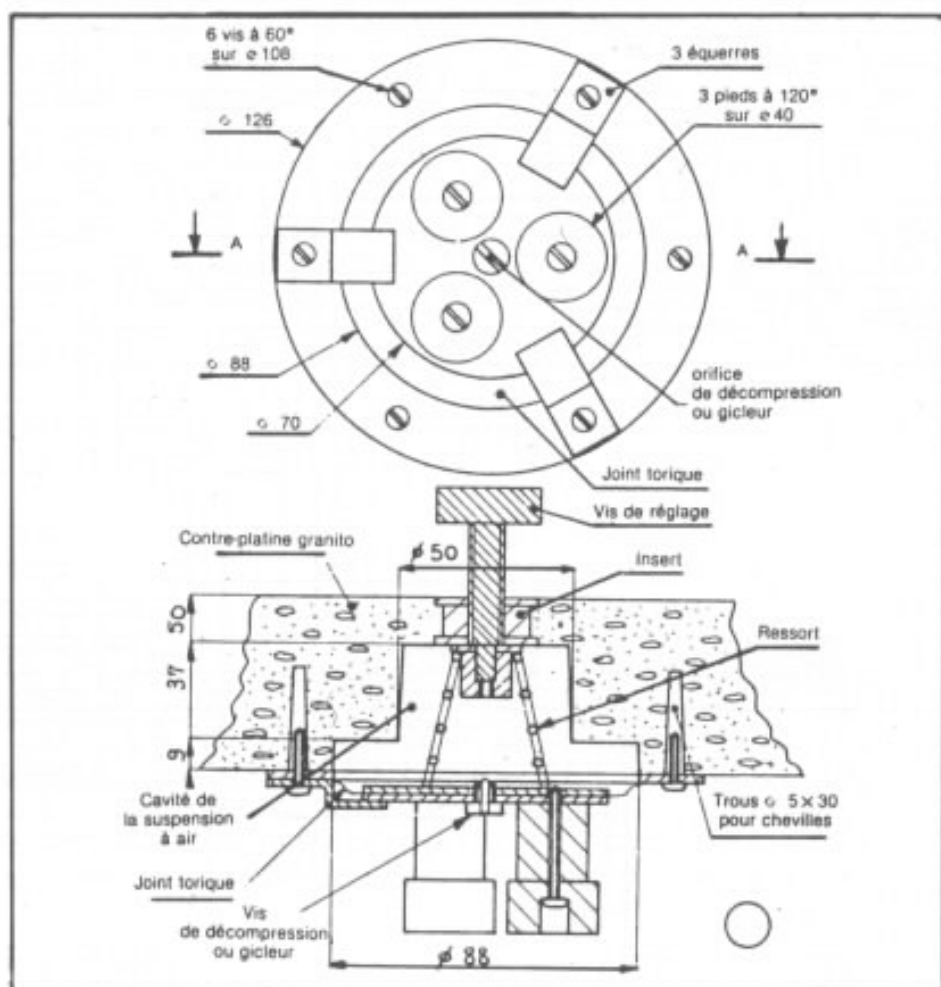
Vue d'ensemble d'un des trois éléments de suspension.
